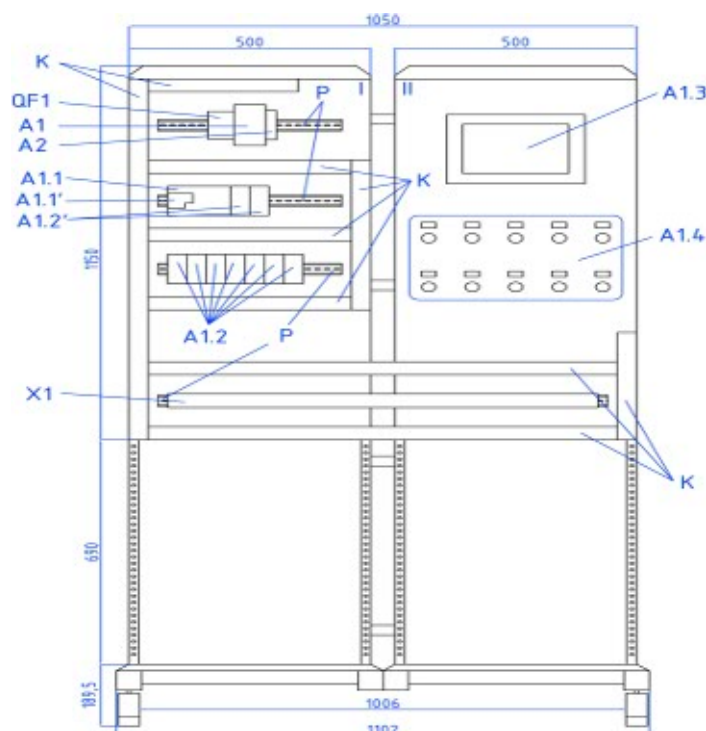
Эскизный чертеж лабораторного стенда:
